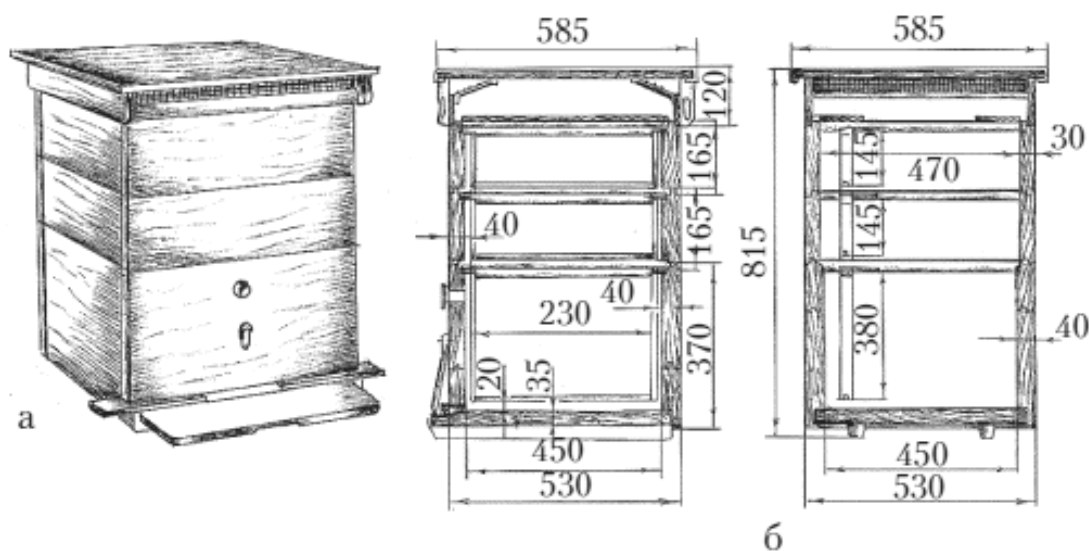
Двухкорпусный улей (размеры в мм): а – общий вид; б – устройство улья б
